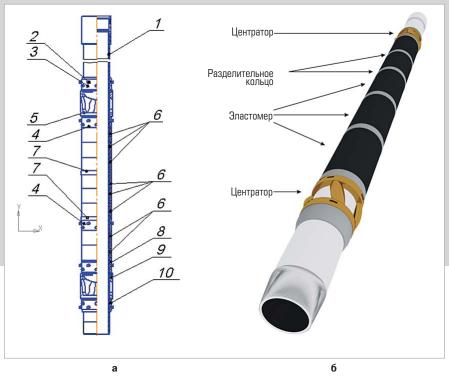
Набухающий пакер: а – сборочный вид; б – вид в аксонометрии
